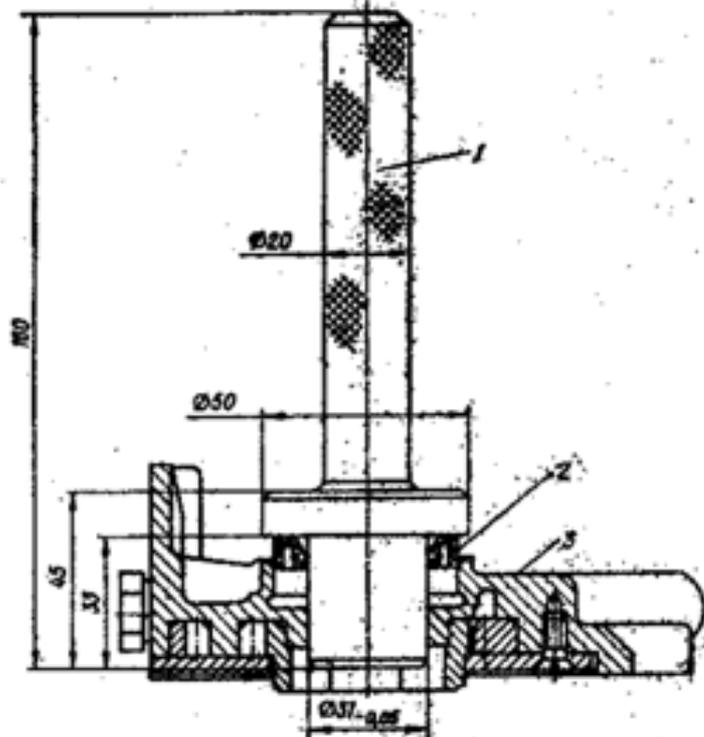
Запрессовка манжеты в корпус масляного насоса: 1 - оправка М9840-879; 2 - манжета; 3 - корпус масляного насоса
